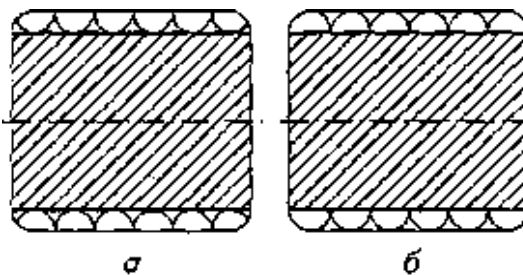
Вид відновлювальної поверхні при різних схемах подачі дротів:
